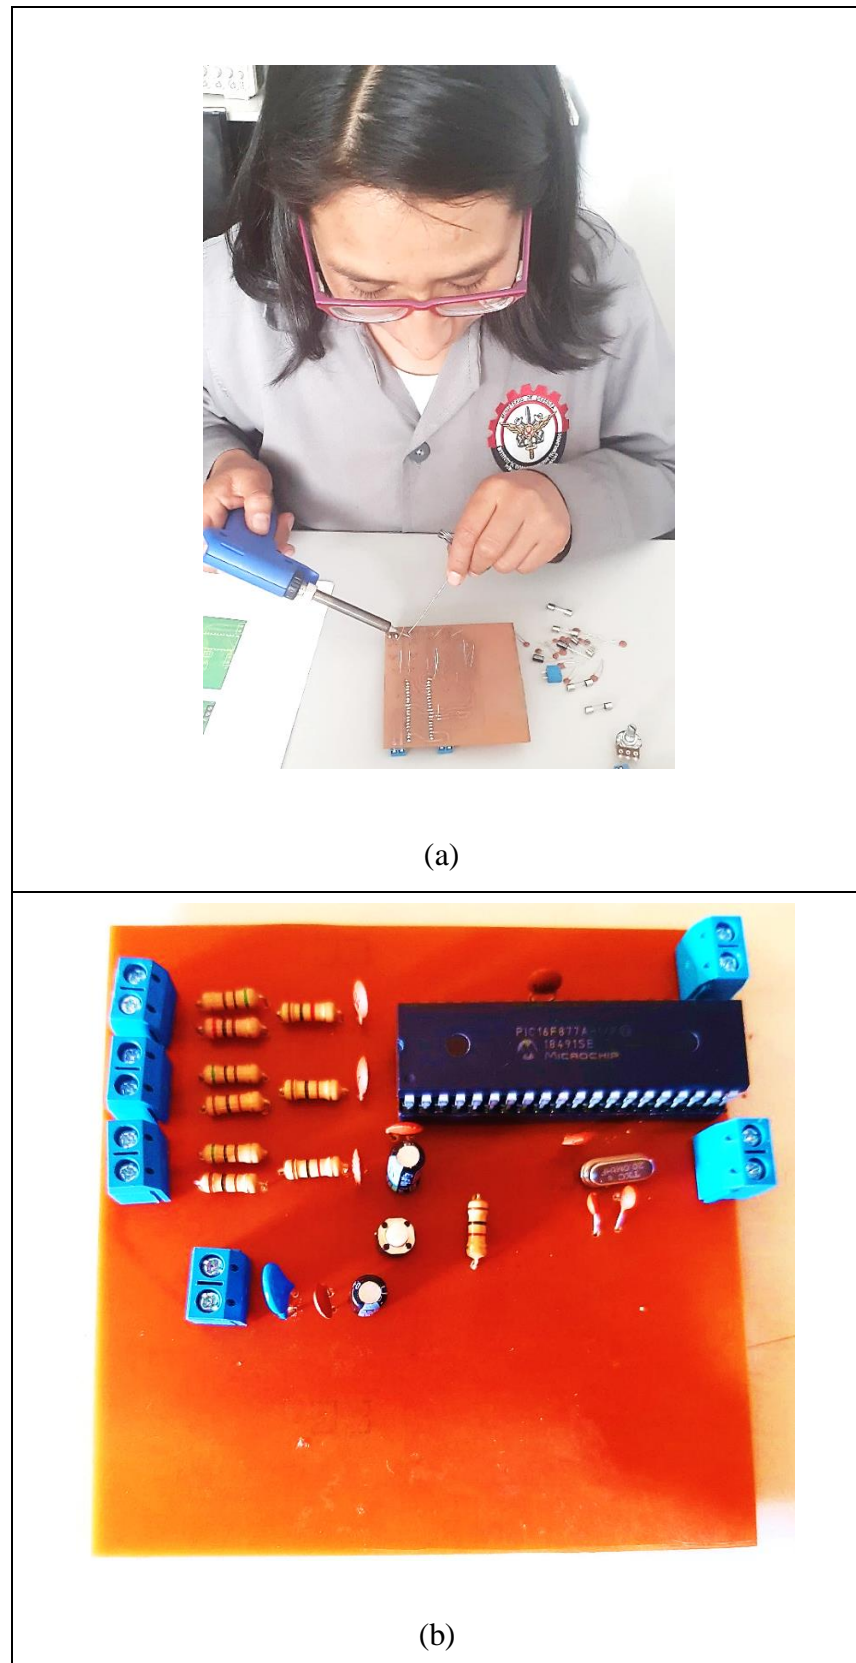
Soldando los componentes, (a) Soldando los Componentes Electrónicos y (b) Placa con los Componentes Electrónicos Soldados.
